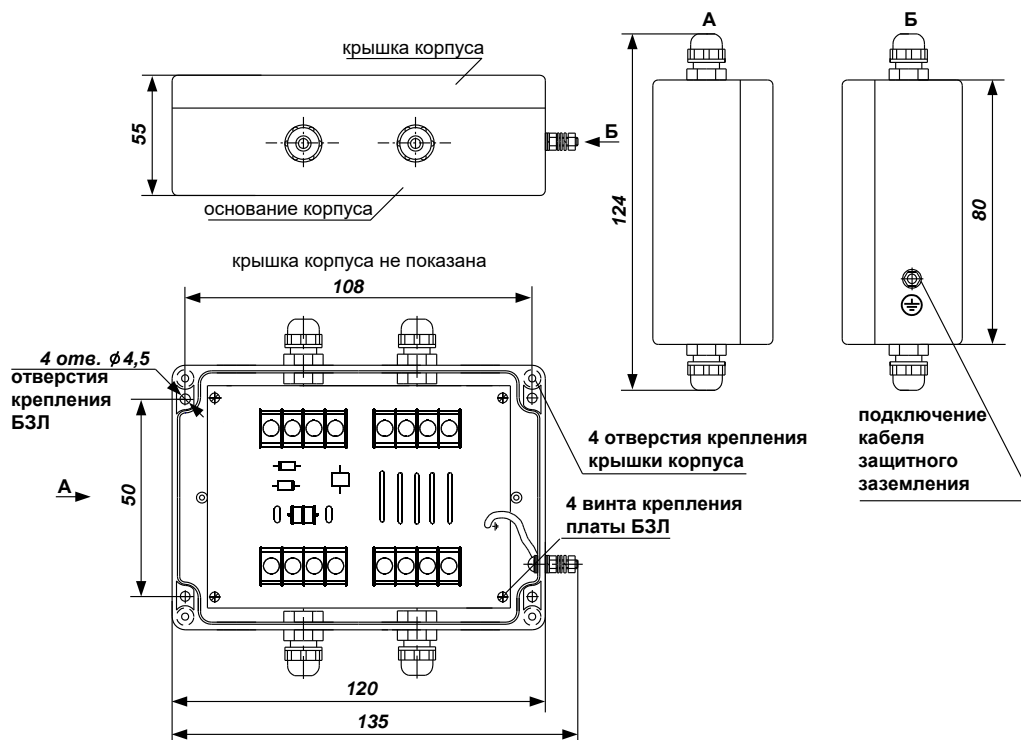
Габаритные и присоединительные размеры БЗЛ-02, БЗЛ-03
